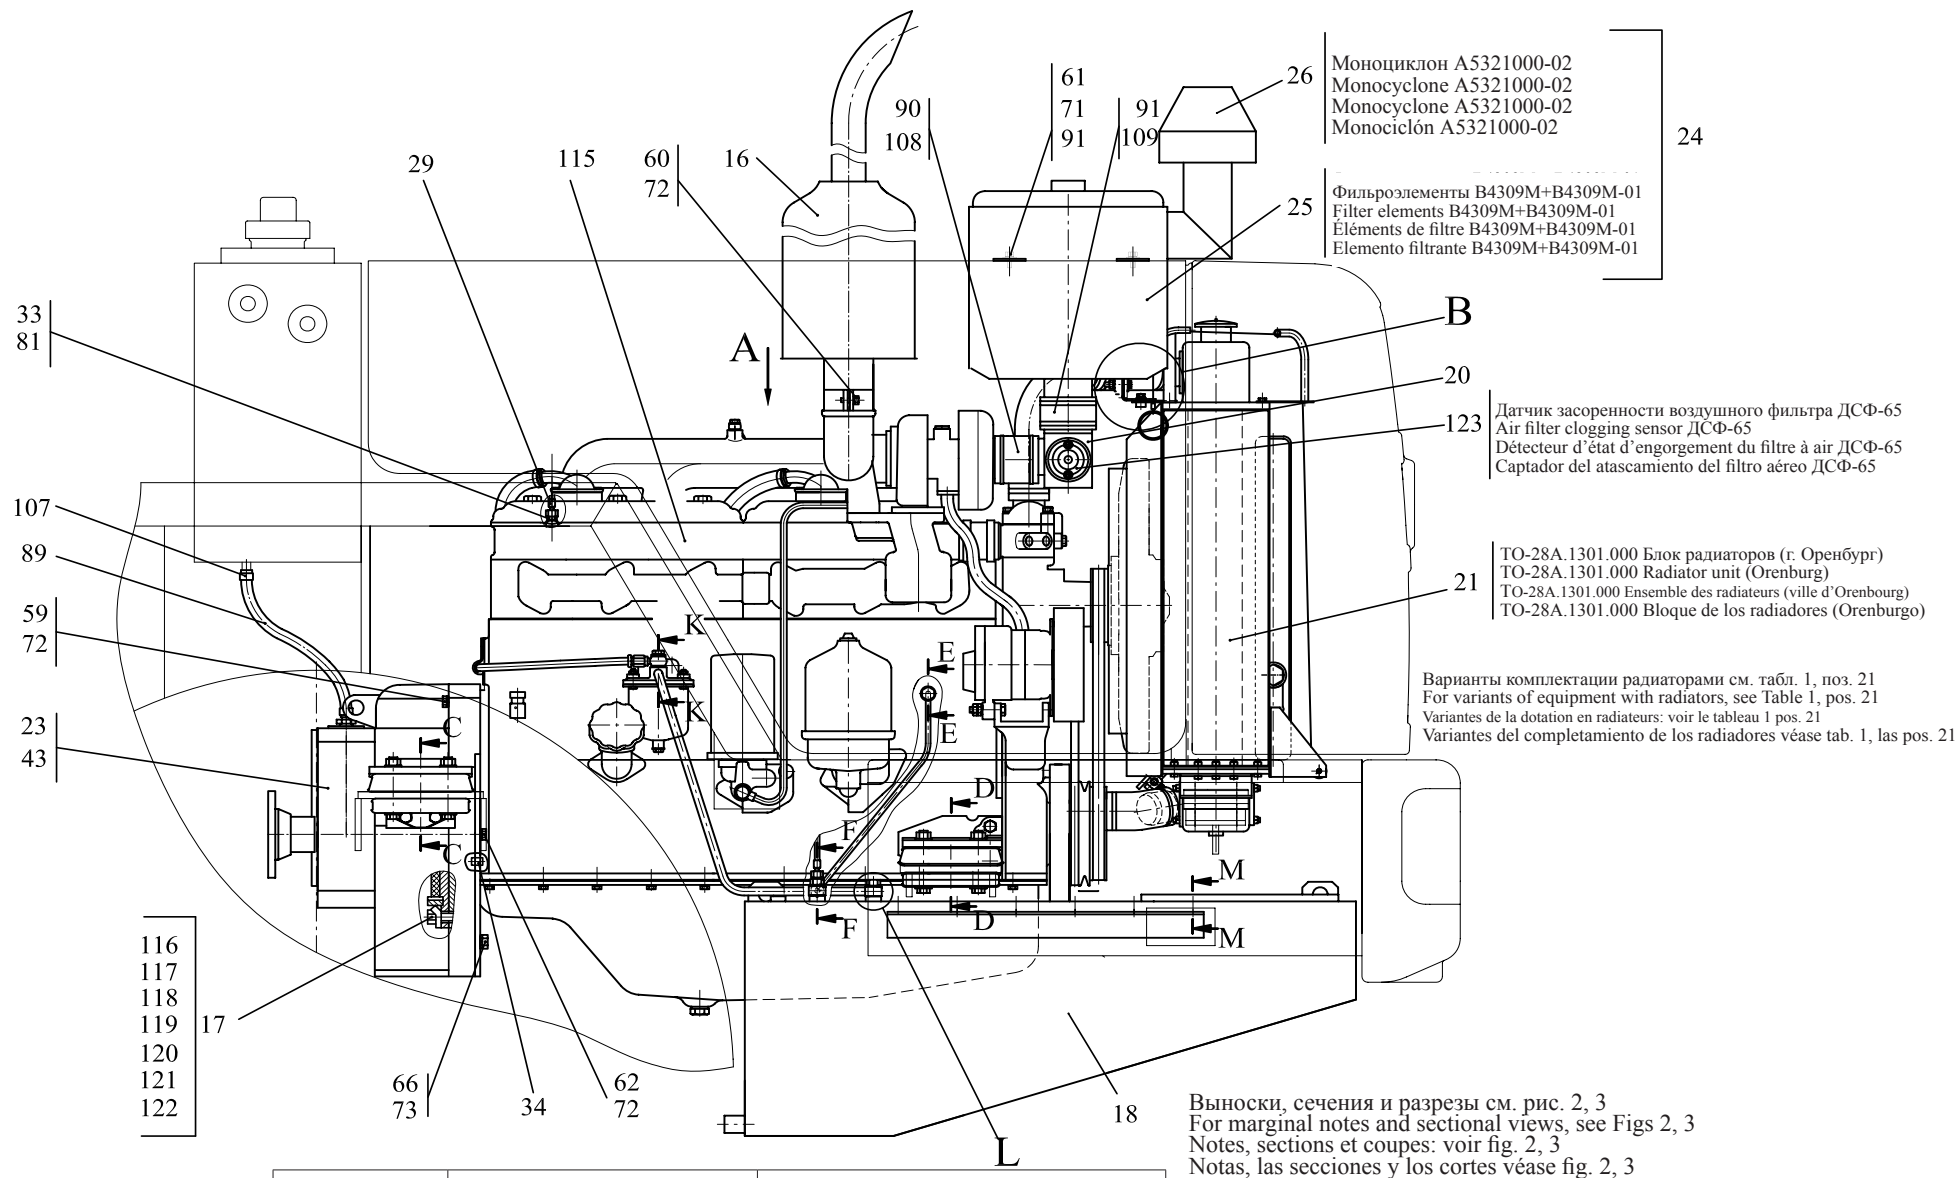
ТО-28А.02.00.000-01	Установка силовая
